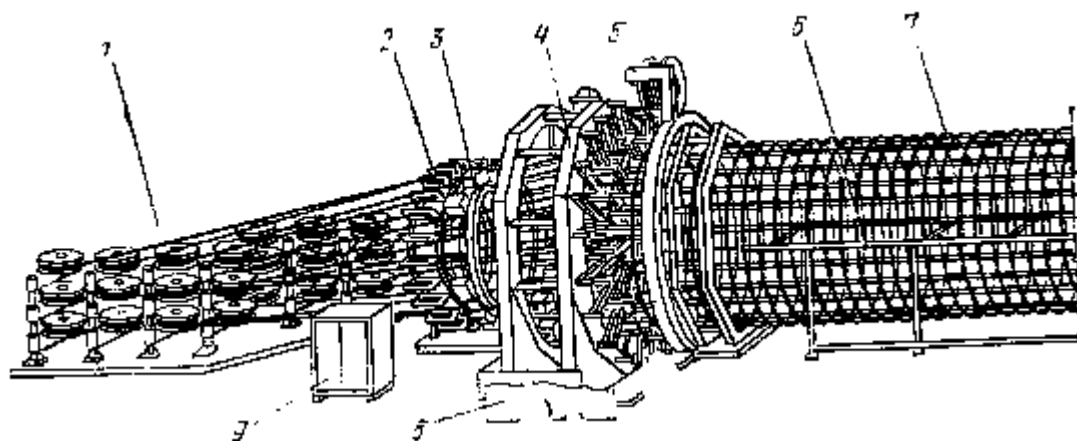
Установка СМ.Ж--;20 для сварки и сборки арматурных каркасов железобетонных труб:
